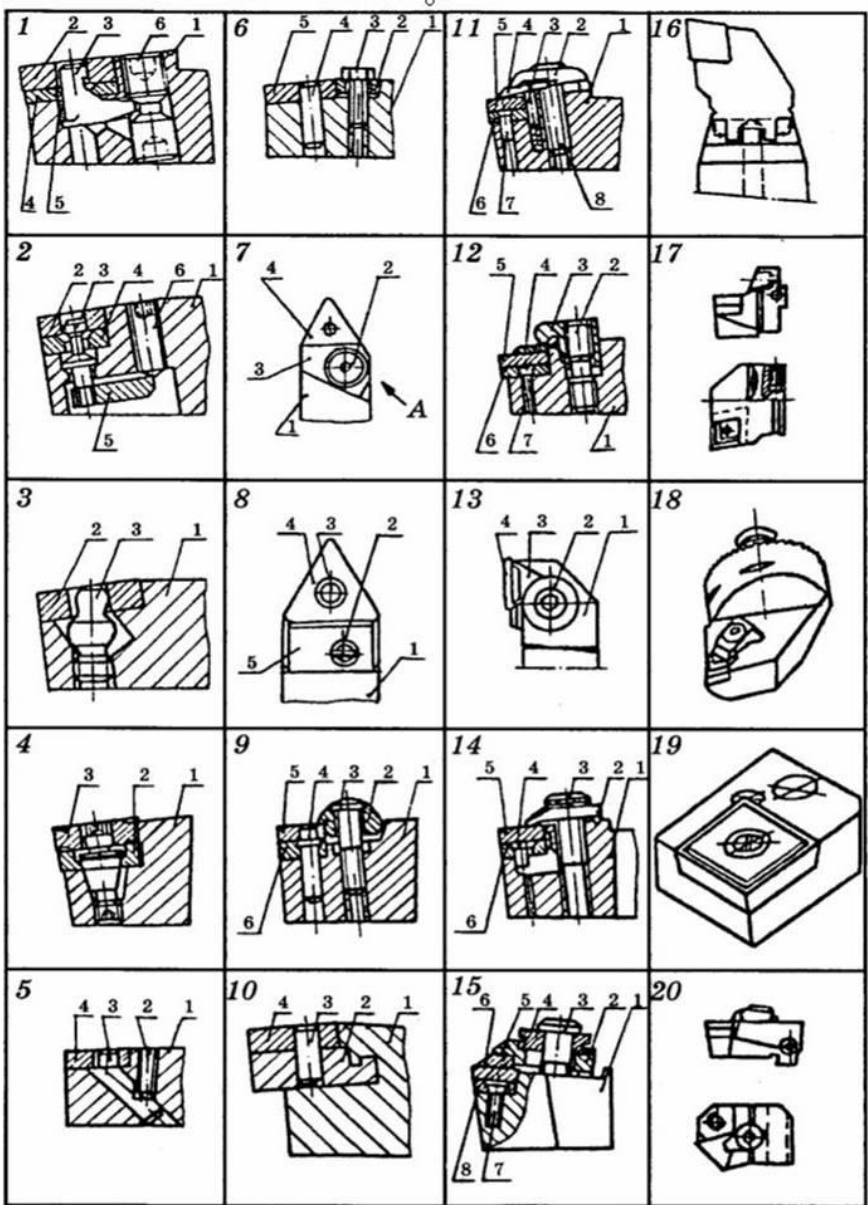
Способы крепления СМП на резцах и резцовых вставках
